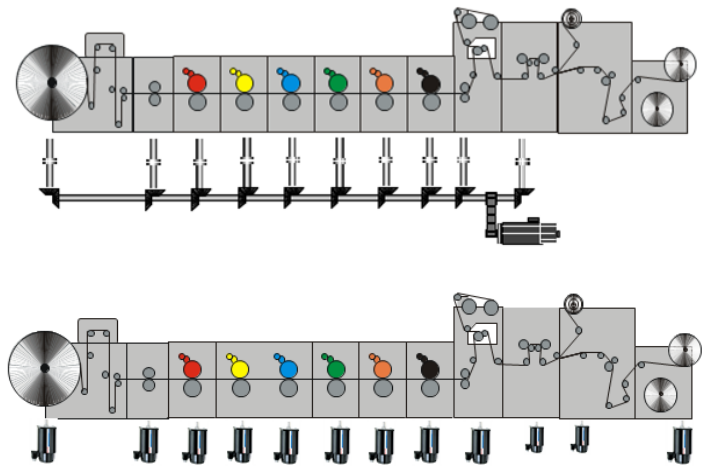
Schema di una macchina per la stampa a sei colori – sei assi – con albero meccanico (sopra) ed *Electronic Line Shafting* (sotto)
